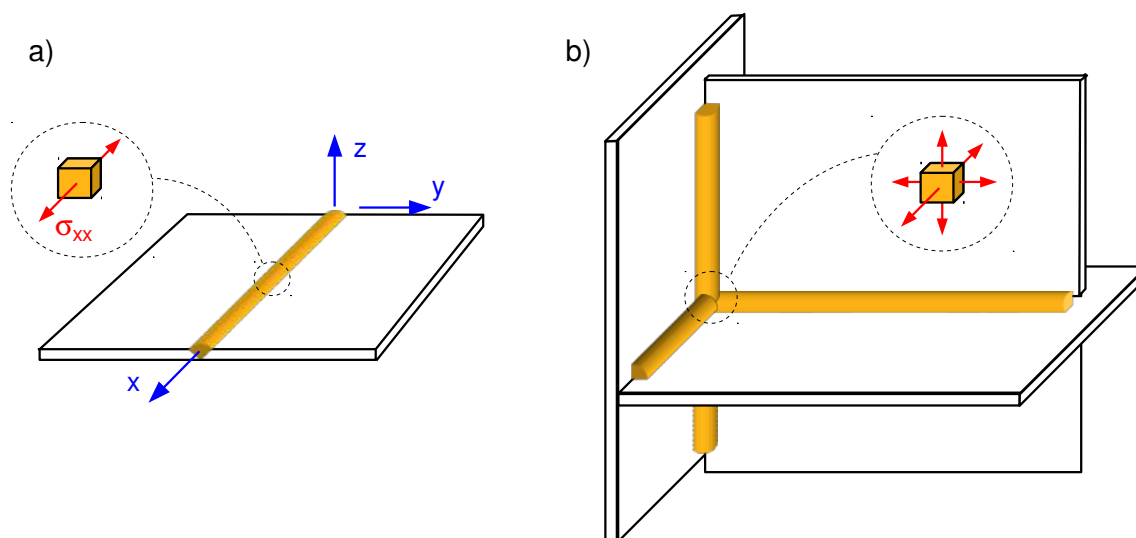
a) Tracción longitudinal en un cordón de soldadura. b) Situación no deseada de tres cordones de soldadura perpendiculares entre sí.
